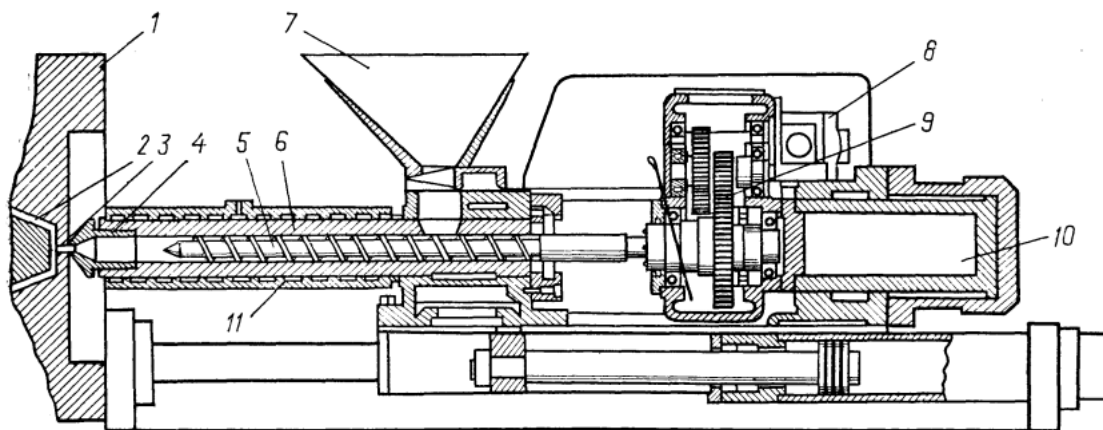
Схема литтєвої машини: 1 – форма; 2 – виріб; 3 – ливниковий канал; 4 – ливникова втулка; 5 – черв'як; 6 – пластикаційний циліндр; 7 – бункер; 8 – привід; 9 – редуктор; 10 – гідравлічний циліндр; 11 – нагрівник
